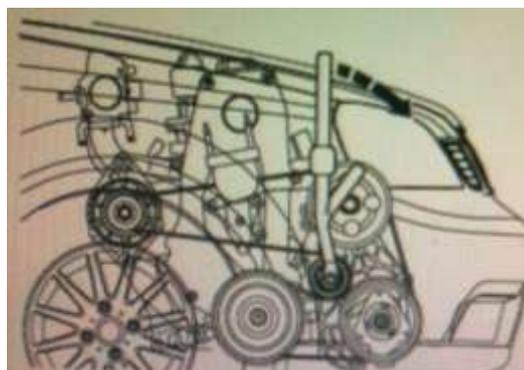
Montaje de Banda Múltiple de Accesorios
